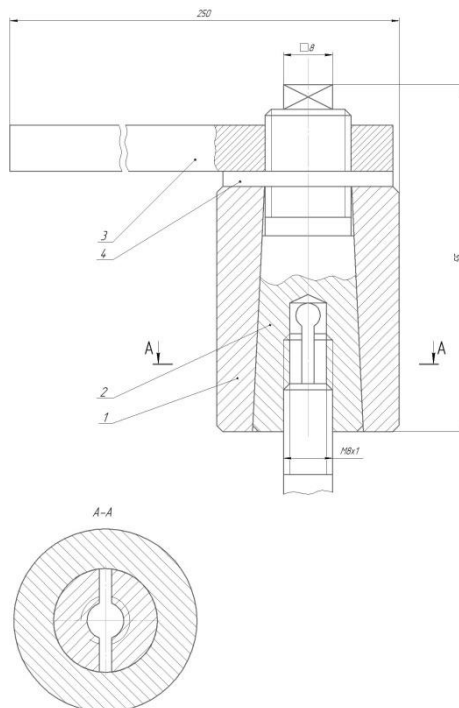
Цанговий пристрій для відкручування шпильок: 1 – оправка; 2 – цанга; 3 – важіль; 4 – шайба.
